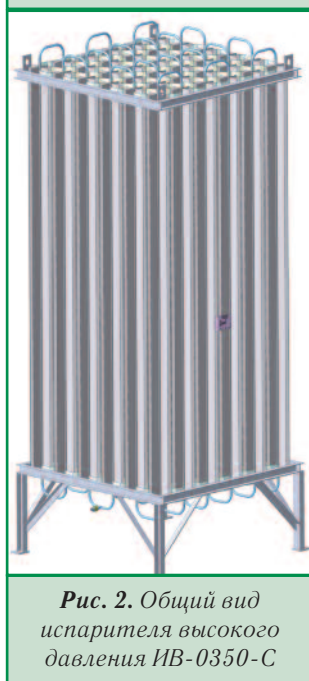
Общий вид испарителя высокого давления ИВ-0350-С
